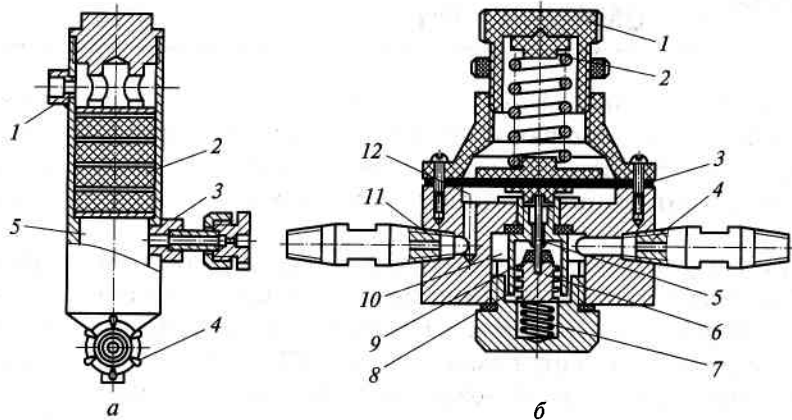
Пневмоустройства для подготовки сжатого воздуха:
